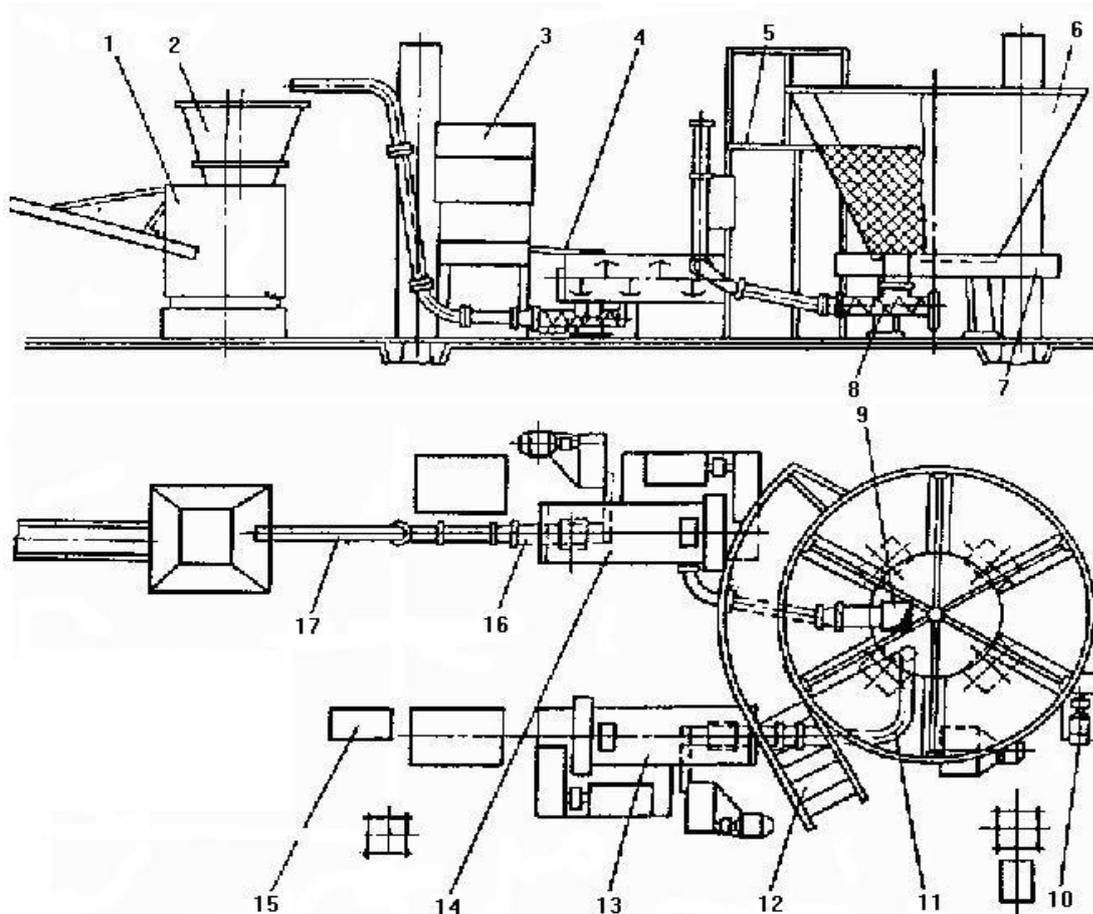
Тестоприготовительный агрегат И8-ХАГ-6:
